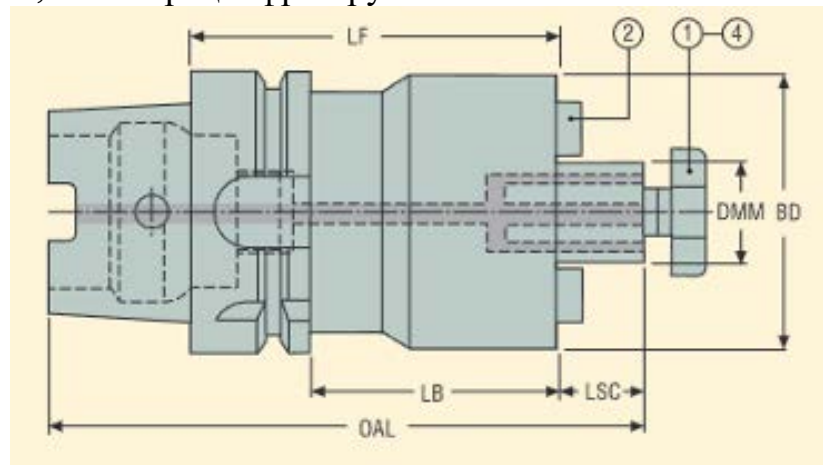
Тримач для торцевих фрез HSKA63-SM22-100-L1[7, ст.23]
